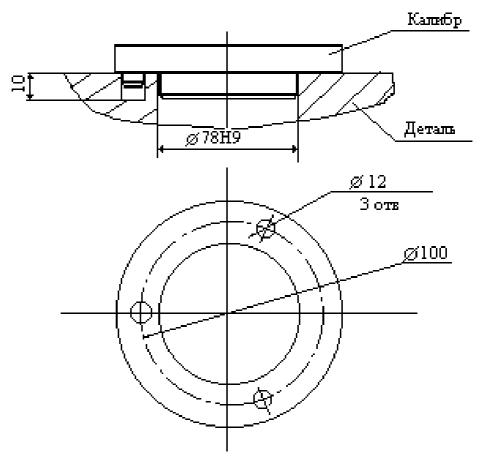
Калибр Определяем размеры направляющей пробки калибра
